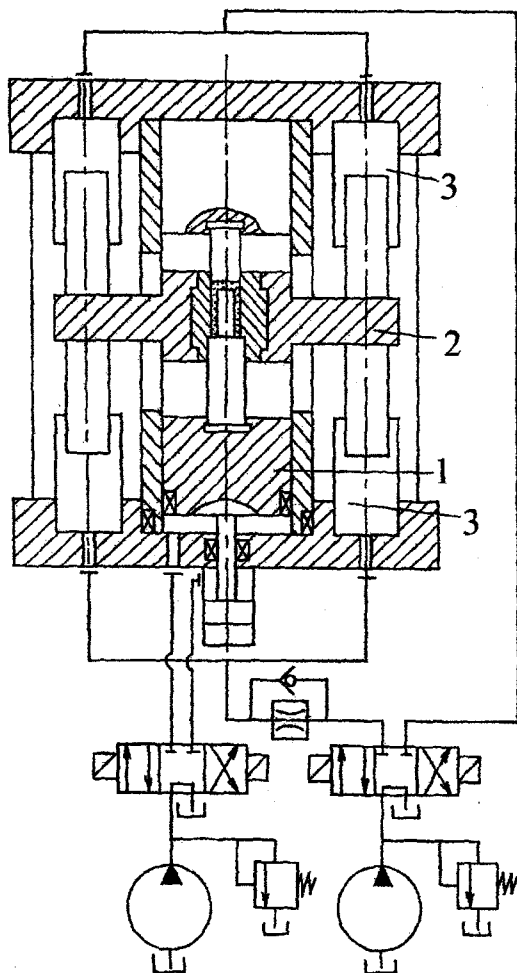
Конструкция пресса для выдавливания с активными силами трения
